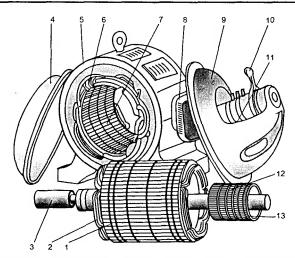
Асинхронный электродвигатель с фазным ротором: 1 — сердечник ротора; 2 — обмотка ротора; 3 — вал; 4 — подшипниковый щит со стороны привода; 5 — корпус статора; 6 — обмотка статора; 7 — сердечник статора; 8 — коробка выводов; 9 — подшипниковый щит со стороны контактных колец; 10 — рычаг короткозамыкающего приспособления; 11 — шеткодержатели внутри щита 9; 12 — контактные кольца; 13 — смещающееся вдоль вала кольцо короткозамыкающего приспособления
